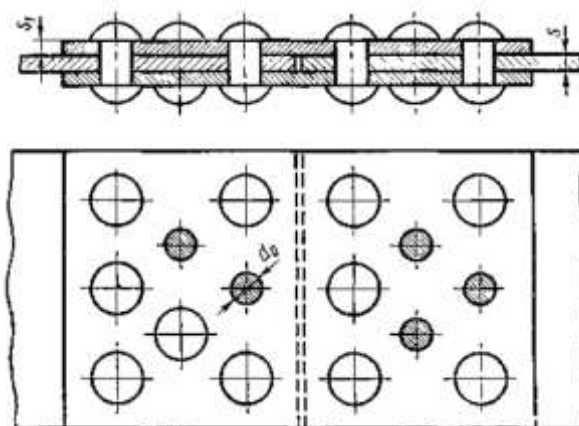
Многорядный двухсрезный шахматный заклепочный шов с двумя накладками
